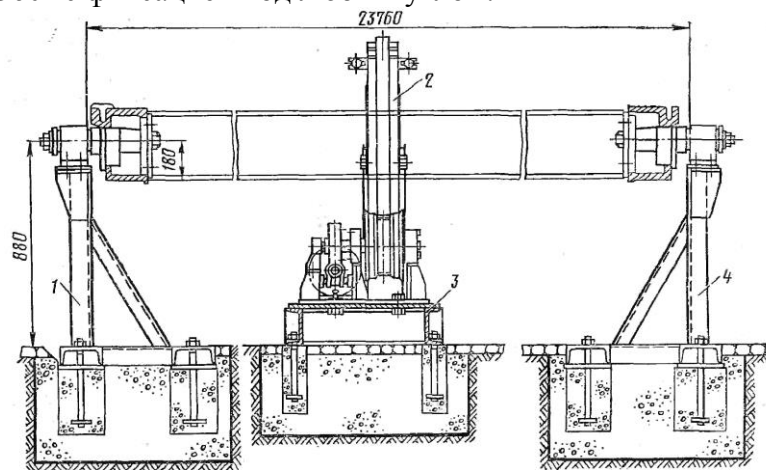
Двухстоечный кантователь для хребтовой балки:
